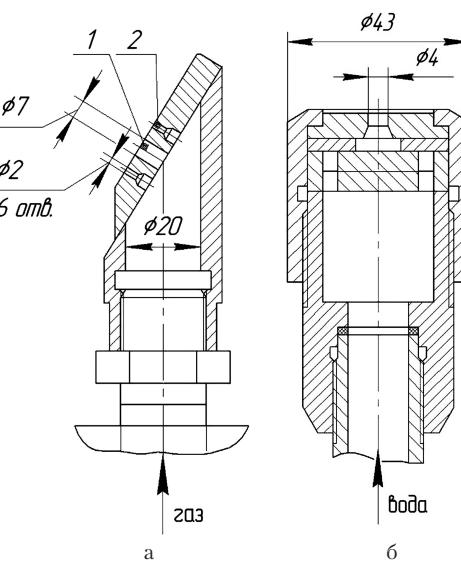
Газовая головка механической форсунки (а) и форсунка (б): 1 – основное сопло; 2 – стабилизаторы.
